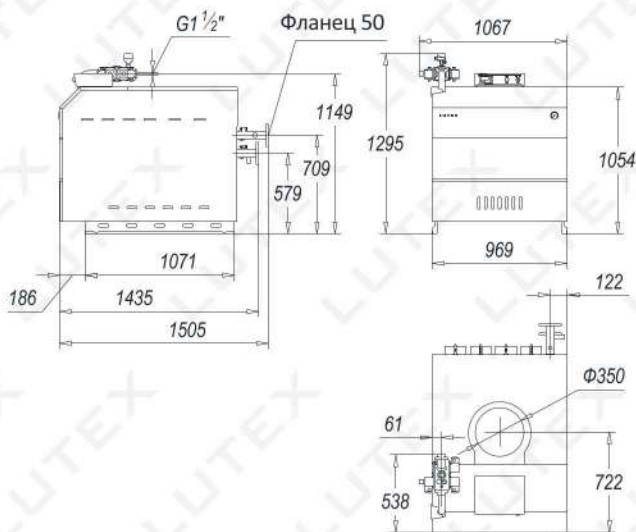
Габаритно – присоединительные размеры AR-S300.
